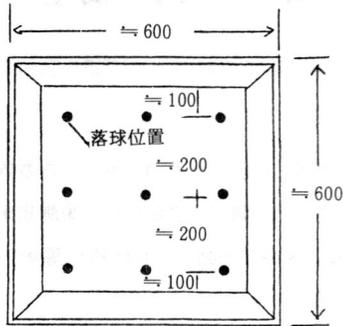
収納庫（シェル）の衝撃試験方法（平面図）
